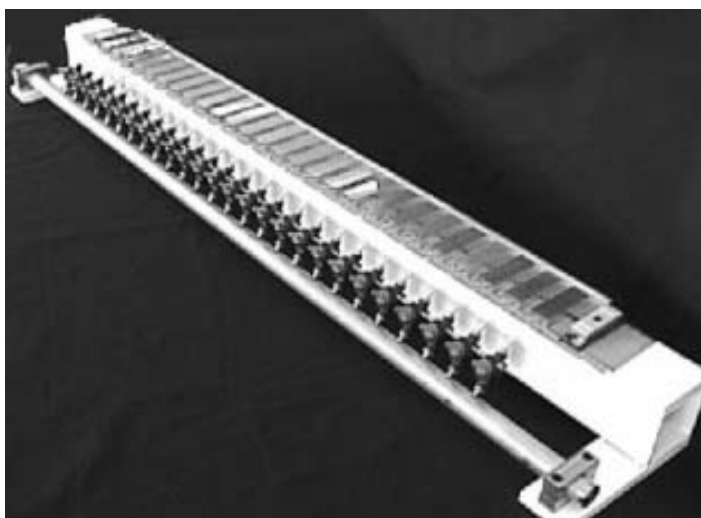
DE MAL VOOR HANDASSEMBLAGE MET KOOLSTOFFRAME EN GLASPLAATJES
